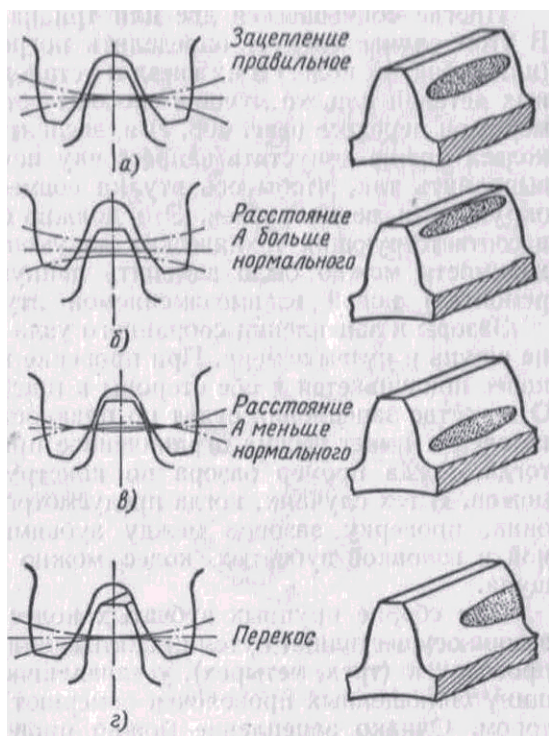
Выявление погрешности монтажа зубчатых колес по расположению пятна контакта: *а* – правильное зацепление; *б* – увеличенный боковой зазор; *в* – уменьшенный боковой зазор; *г* – перекос осей зубчатых колес
